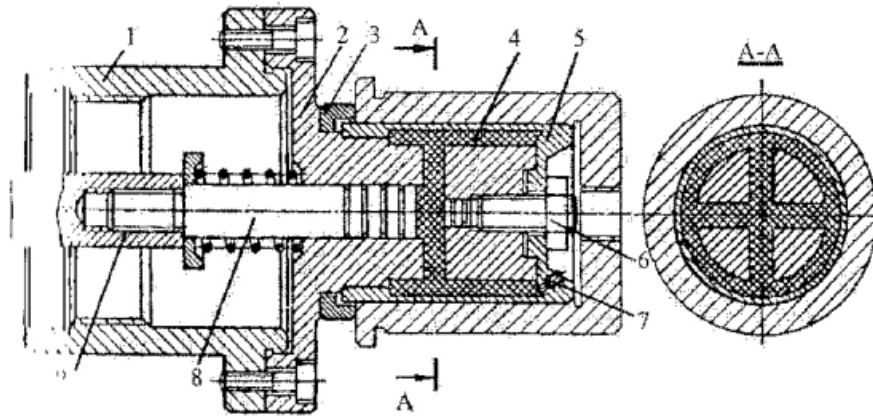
Конструкция пневматической оправки с гидропластом.
